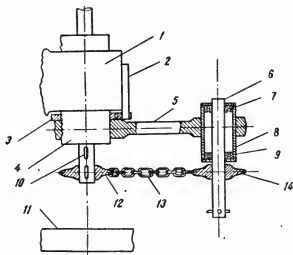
Приспособление к вертикально-сверлильному станку для расточки ступиц колес сеялок.
